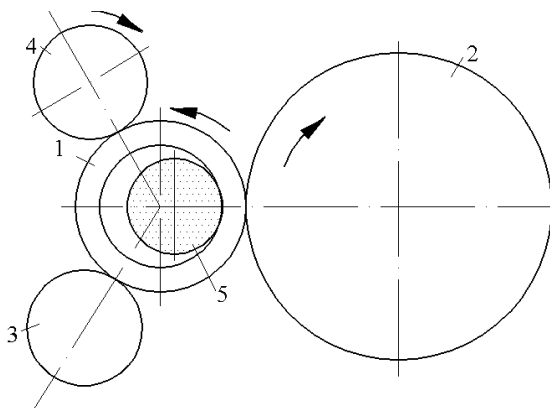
Схема обробки доріжки кочення зовнішнього кільця роликпідшипника
